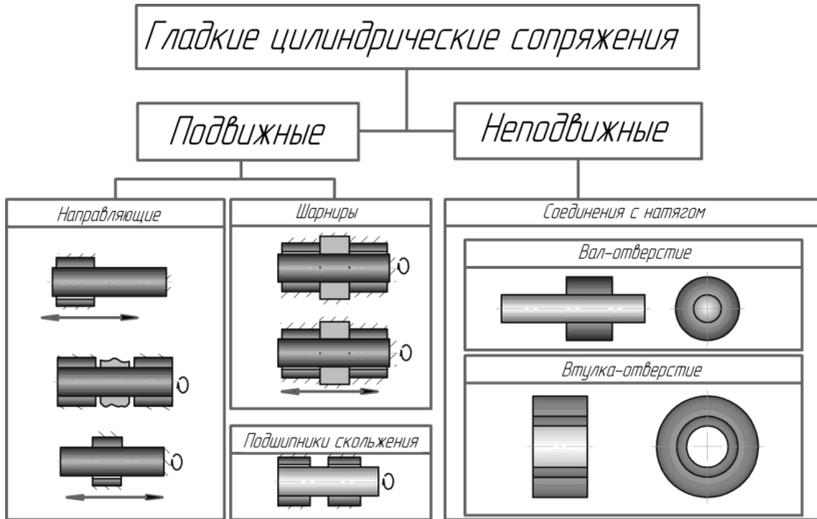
Конструктивные схемы гладких цилиндрических сопряжений
